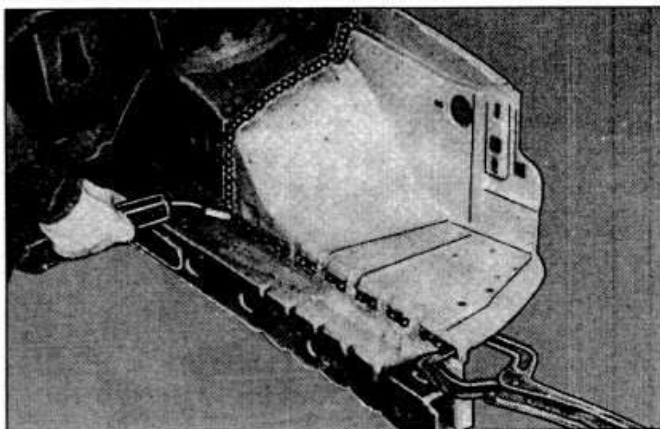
Приварка надколесного кожуха к лонжерону
